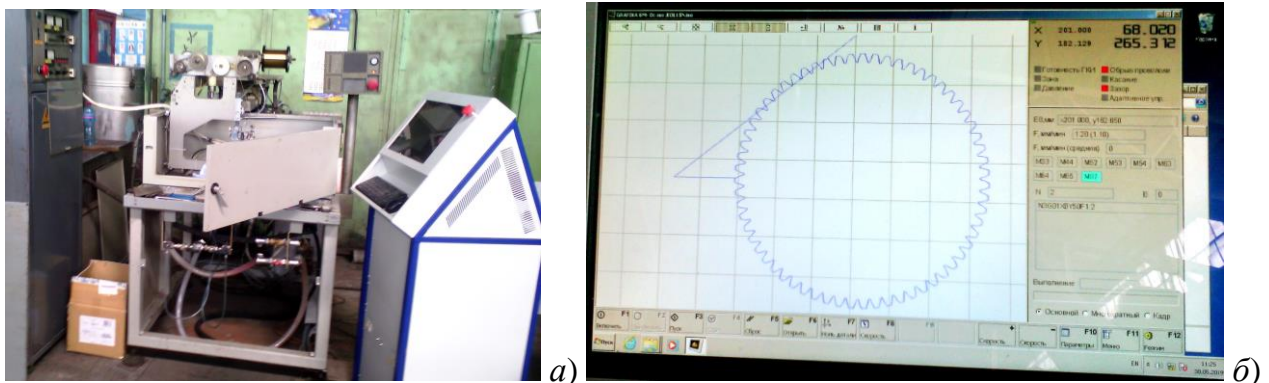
Загальний вигляд верстата для комбінованої обробки (а)
